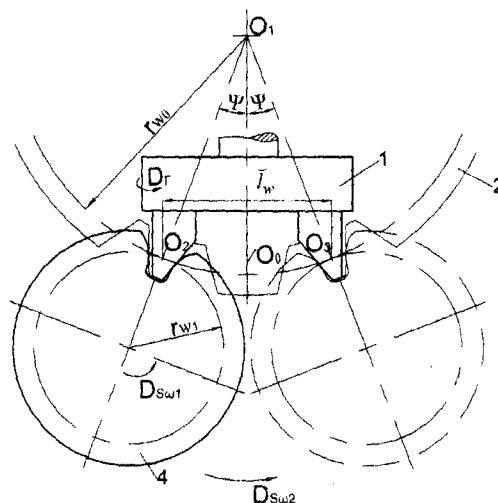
Схема формообразования зубьев цилиндрического колеса
